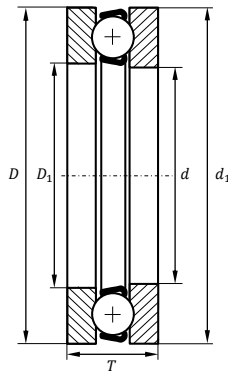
Schnittansicht des Axialrillenkugellagers 51305.
